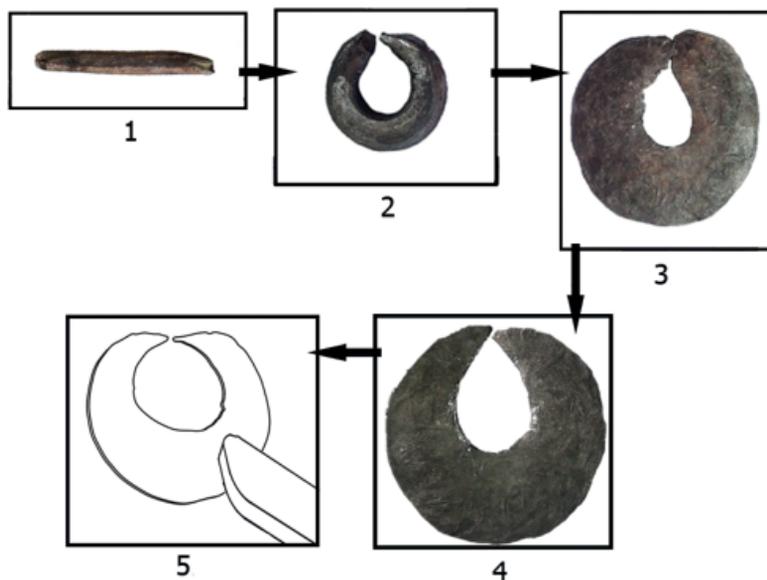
Реконструкция последовательности операций при изготовлении серьги в форме полумесяца (экз. № 3) из могильника Дялян: 1 – заготовка в виде прутка; 2 – заготовка после скручивания; 3 – расплюснутая заготовка; 4 – заготовка с обрезанными ножницами излишками металла; 5 – нанесение декоративных углублений и заглаживание абразивом.
